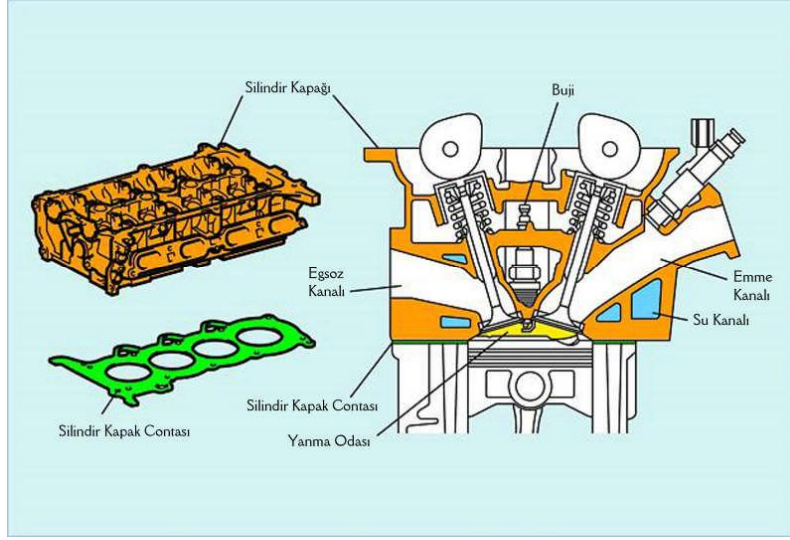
Silindir kapağının motor üzerindeki yeri
